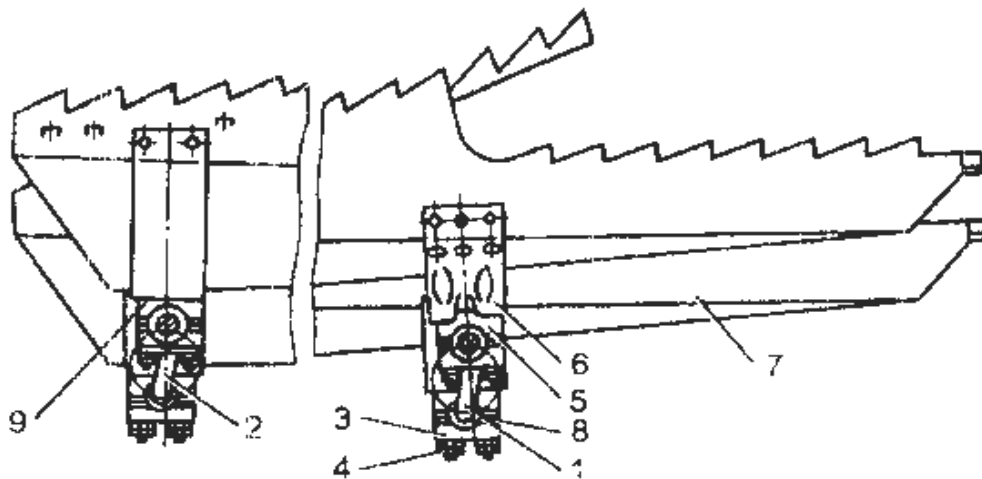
Клавишный соломотряс: 1 – вал коленчатый ведущий; 2 – вал коленчатый ведомый; 3, 5 – подшипники скольжения; 4 – гайка; 6 – кронштейн задний; 7 – клавиша; 8 – прокладка; 9 – прокладка
